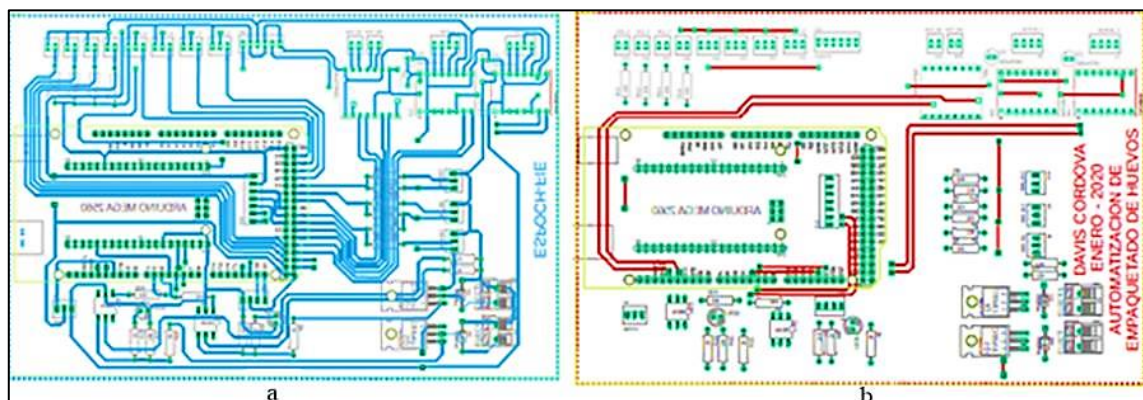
Diseño PCB del controlador del ACEPS a) Vista inferior b) Vista superior
